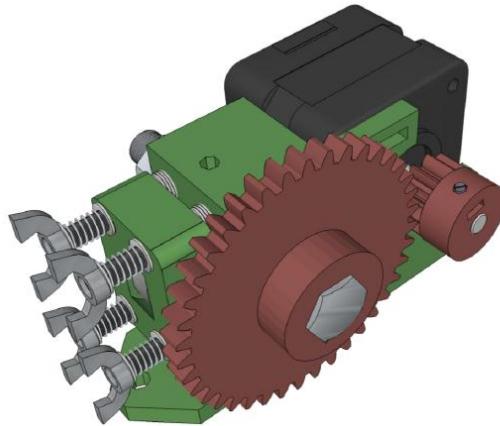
Colocación Montaje del motor y ensamblado de los engranajes. Extrusor ensamblado
